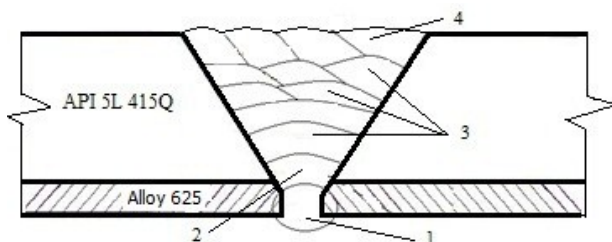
Последовательность комбинированной сварки стыка плакированной трубы. 1-корневой слой (GTAW); 2-горячий (GTAW); 3-заполнение разделки (SMAW); 4- облицовочный слой (SMAW)
